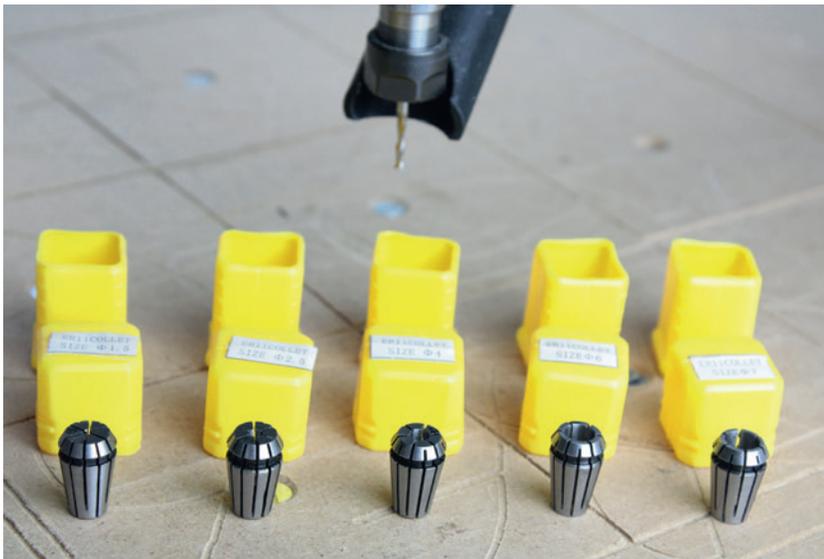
Für jeden Schaftdurchmesser die passende Spannanzge (bei ER11 von 1 bis 7 Millimeter)
